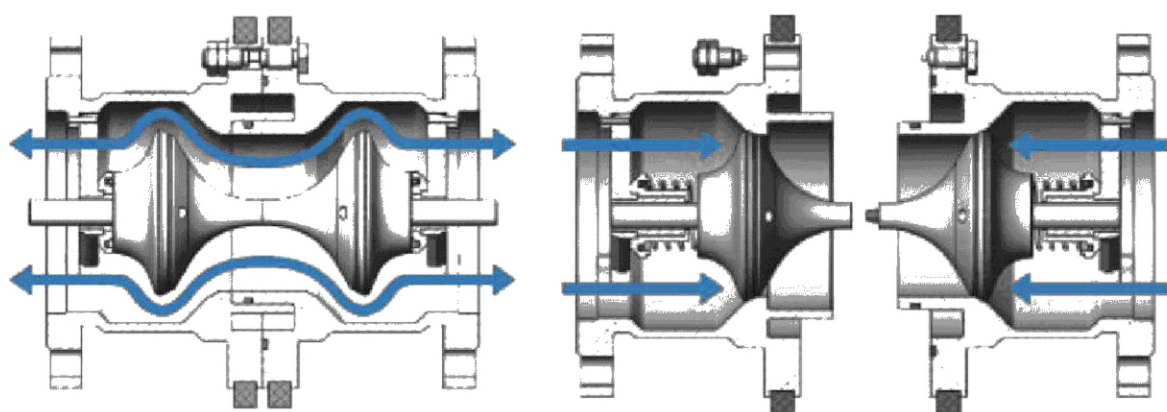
Эскиз схемы работы муфты аварийного разъединения
